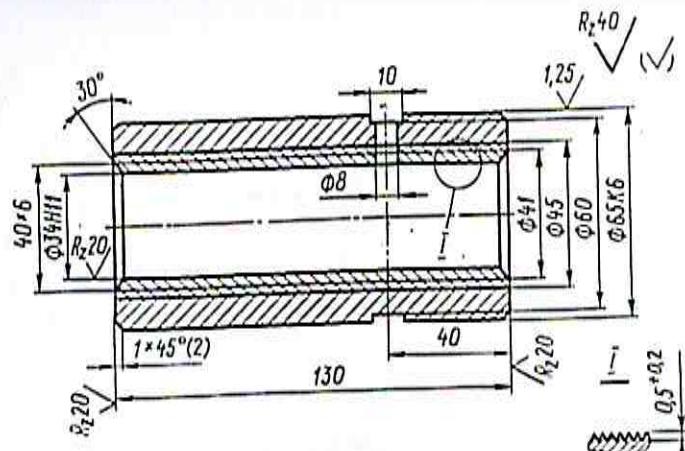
Гайка биметаллическая. Деталь 6М82.7.102
